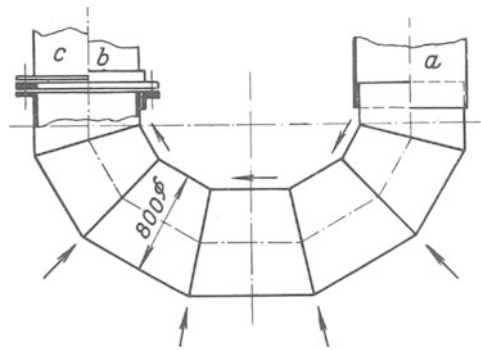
Geschweißter großer Rohrbogen.
